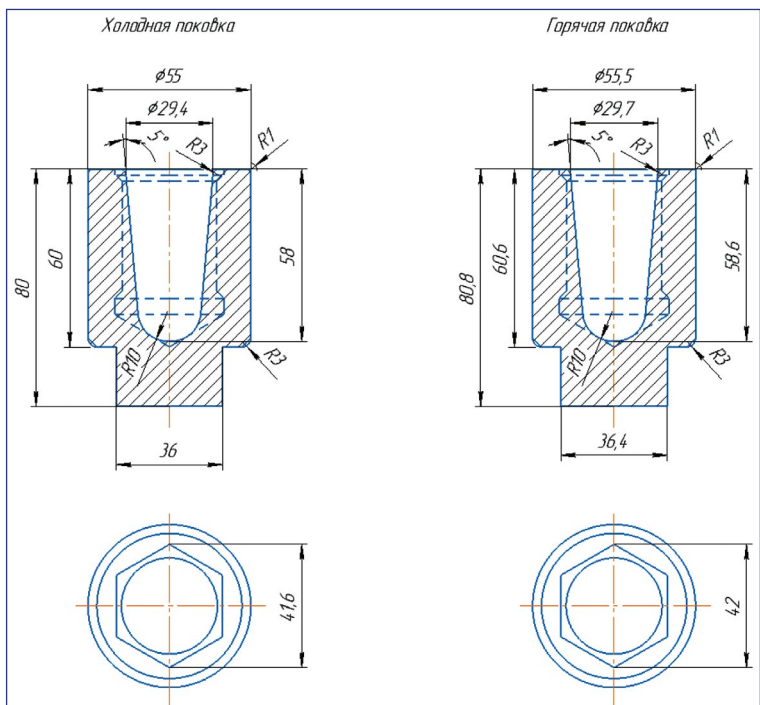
Холодная и горячая поковка колпачковой гайки БМ 36
